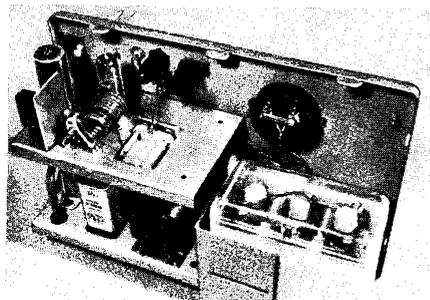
Der innere Aufbau des Senders. Die beiden Bohrungen auf dem freien Teil des Sender-Chassis dienen zur Befestigung des Oberwellenfilters. Rechts daneben der 6-V-Akkumulator
